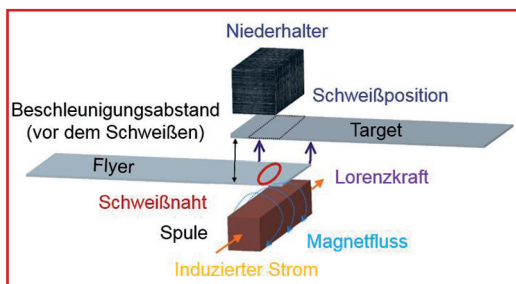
Prinzipskizze des Magnetimpulsschweißens (MPS)
